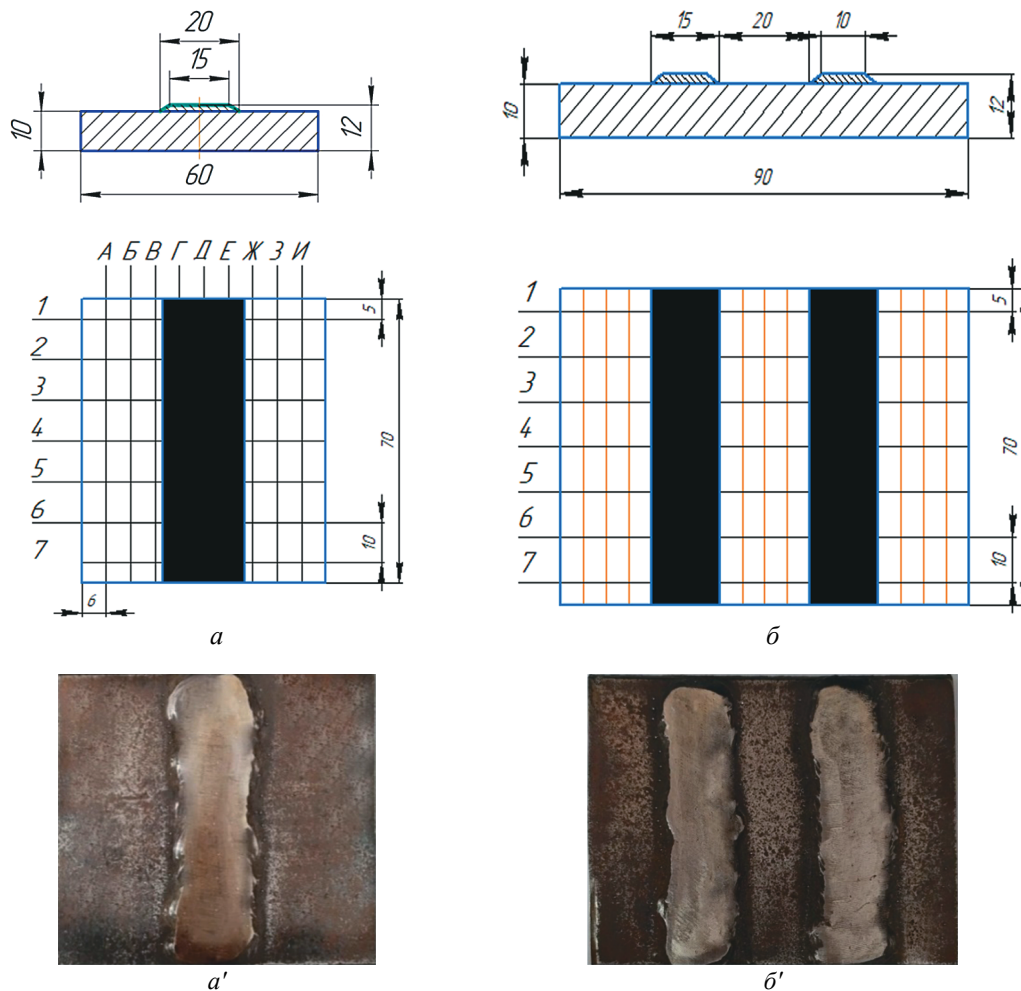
Схема измерений HRC армированных образцов одним валиком (а) и двумя валиками (б); опытный образец с одним валиком (а') и с двумя валиками (б')
